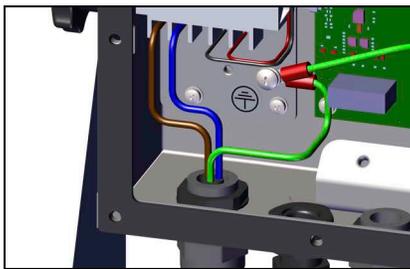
Vorinstallierte AC-Leistungsverdrahtung
